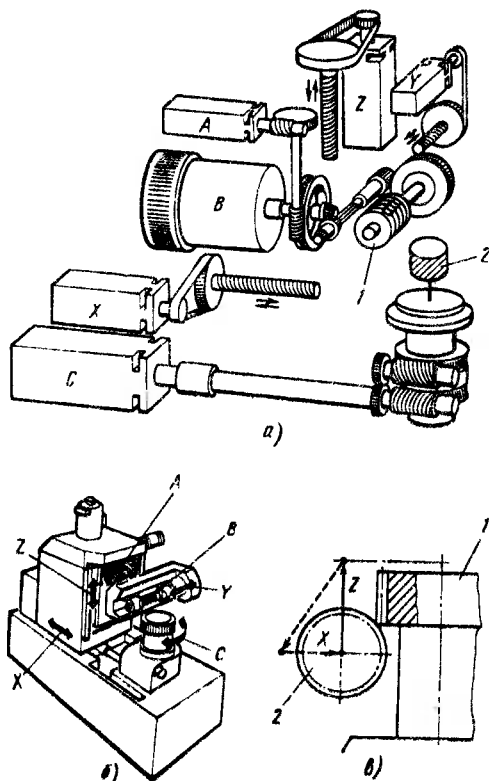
Зубофрезерный станок с ЧПУ:
